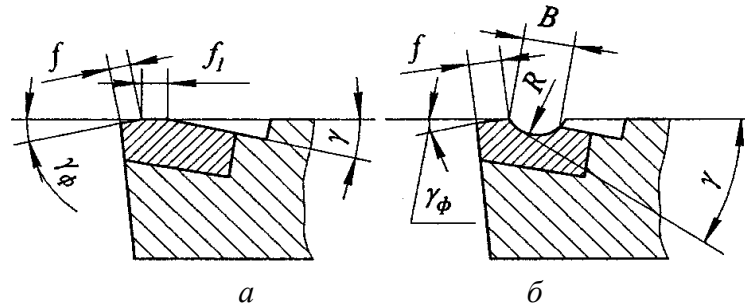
Форма передньої поверхні різців: а - плоска з фаскою; б - криволінійна з фаскою
